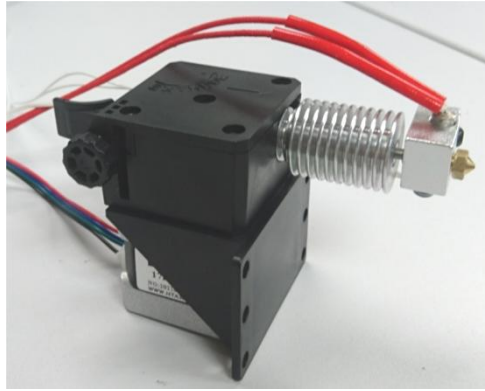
Sistema de extrusión de la impresora ensamblado al completo.
